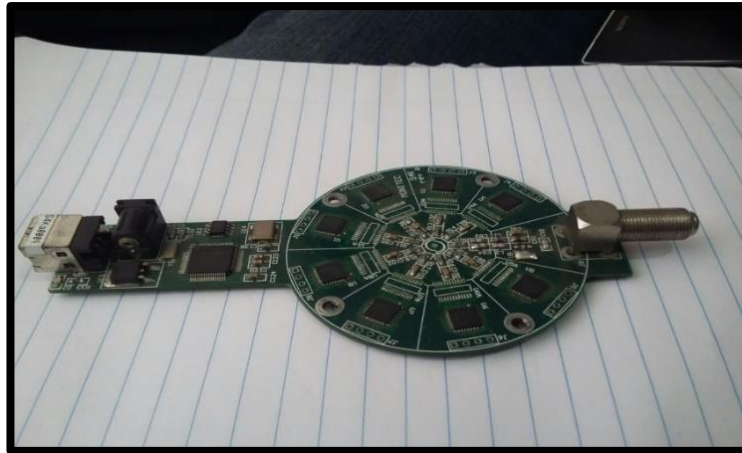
Circuito PCB de 8 sintonizadores FM/AM.
